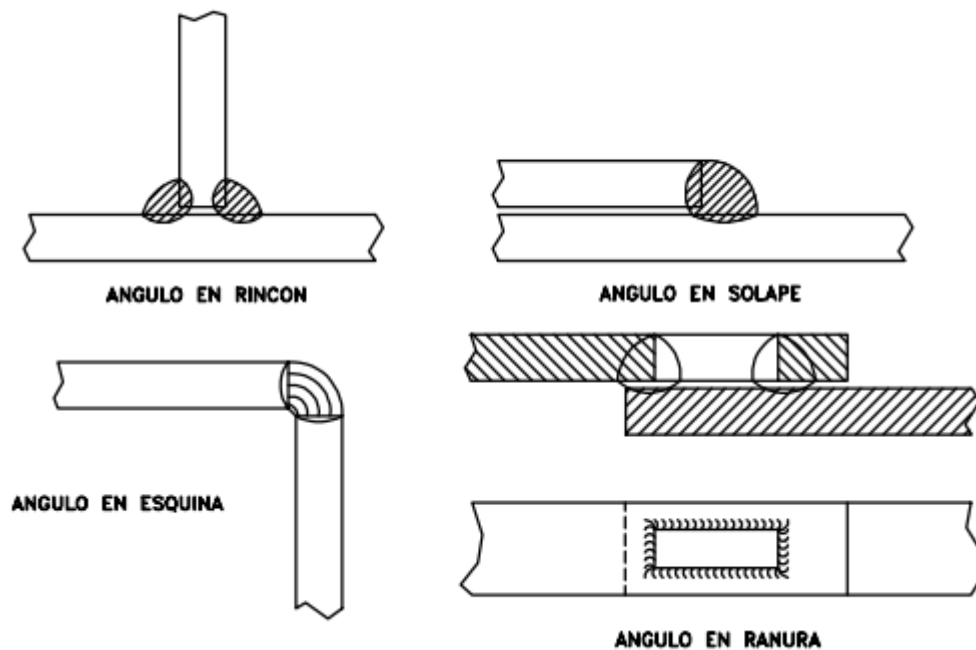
Soldadures en angle (Font: Universidad de Castilla la Mancha)
